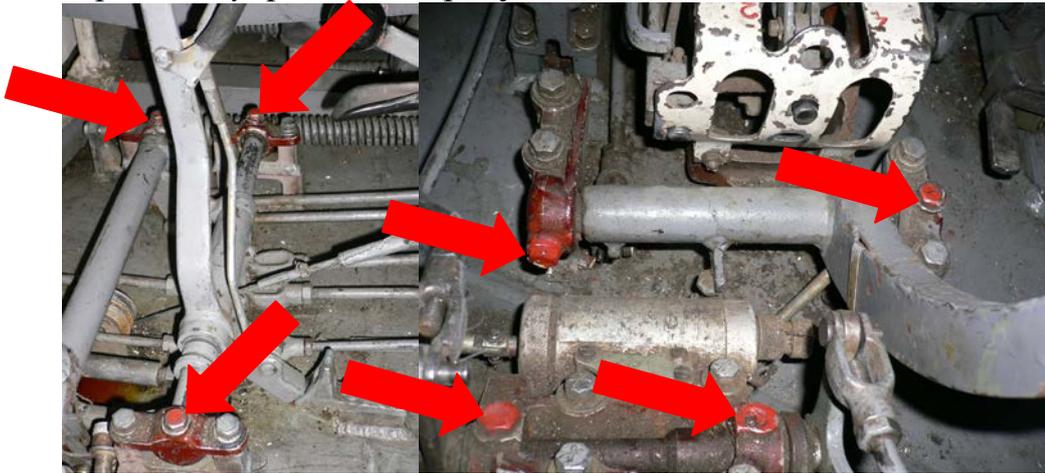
Смазка переходных валиков приводов управления БМД-2
